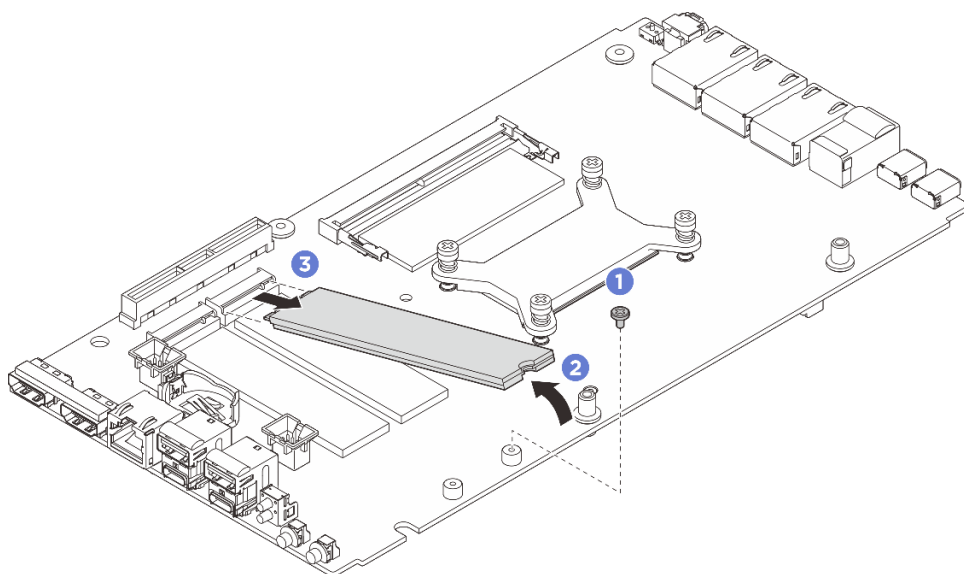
Entfernen des M.2-Laufwerks (Formfaktor 22110)
